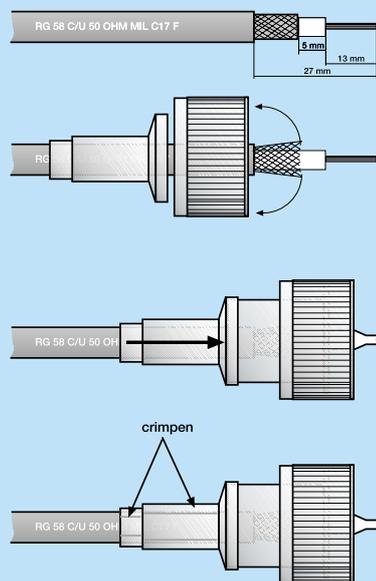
(links): Montagebeispiel für PL-Stecker mit Crimpmontage
